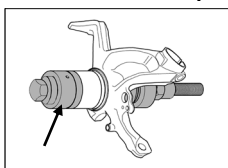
KL-0039-1002 - Aufnahmeadapter für Spannmutter und Druckspindel
